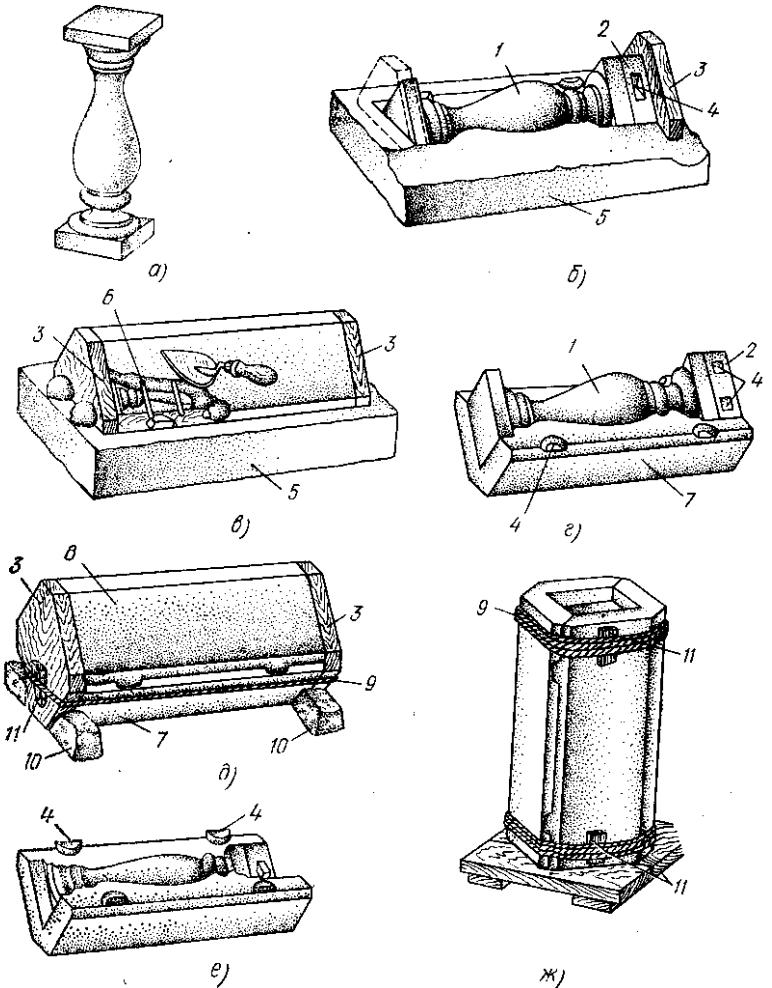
Кусковая форма для изготовления гипсовой балюсины:
